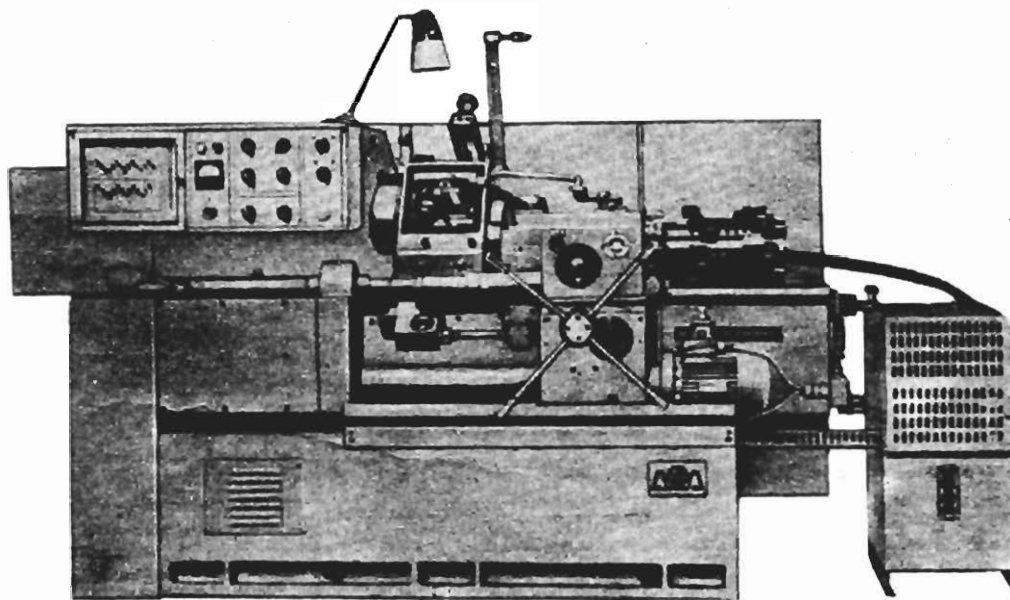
Токарно-револьверные станки 1Г340, 1Г340П
